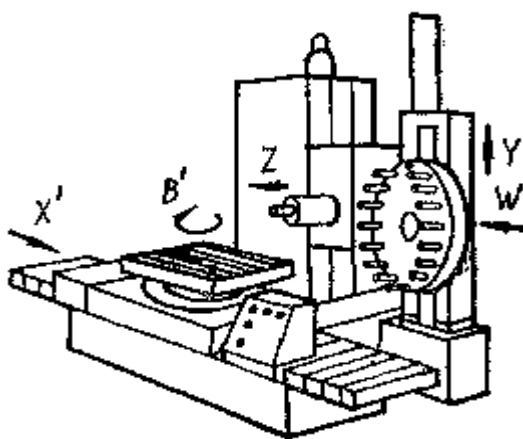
Компоновка горизонтально - розточного верстата.
